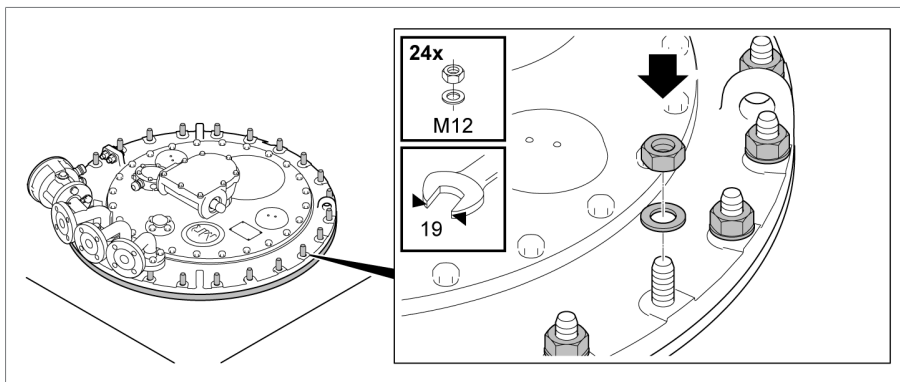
Laststufenschalterkopf mit Aufbauflansch verschrauben
